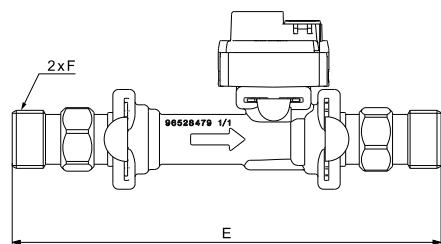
Размеры, VFS, 1-20 л/мин, с адаптерами
